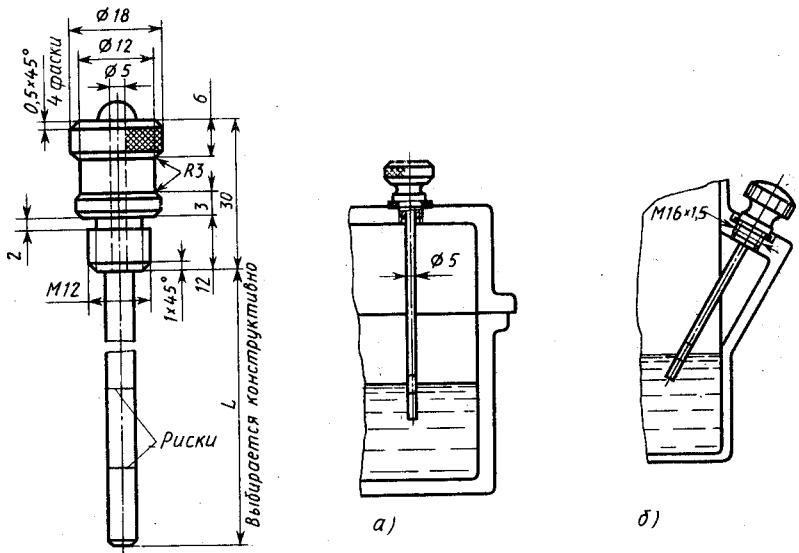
Железный указатель и способы его установки на корпусе:
